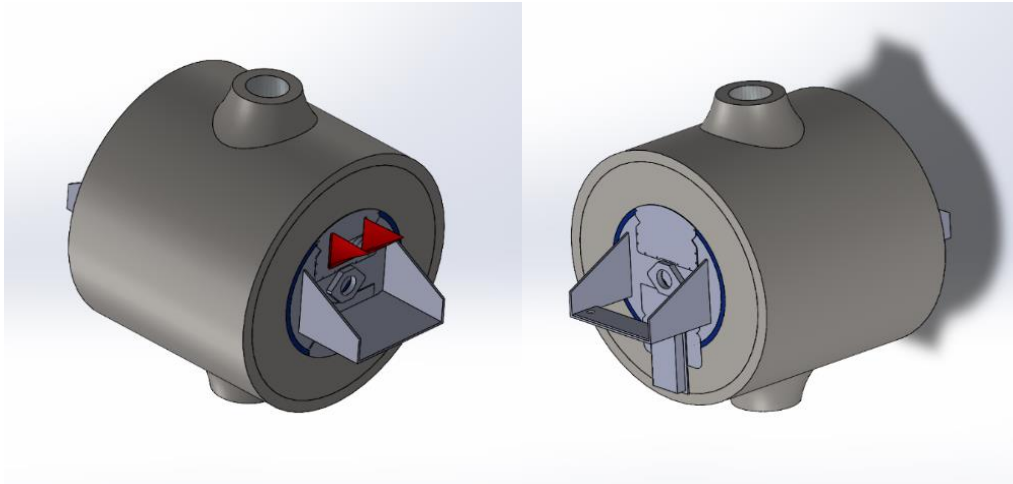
3D-απεικόνιση του Assembly του στροφείου
